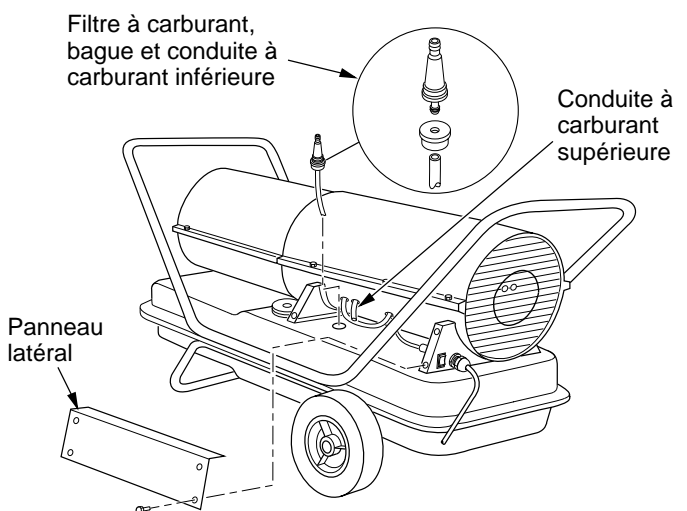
Dépose du filtre à carburant, Modèle GK30
